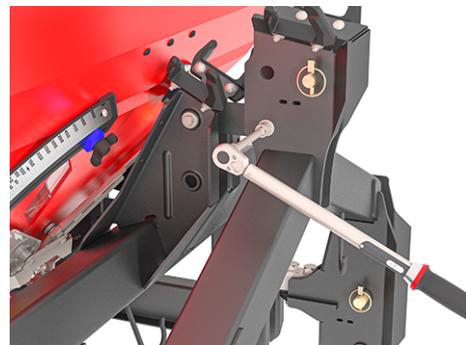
Befestigung des Zugstabes am Wiegerahmen
